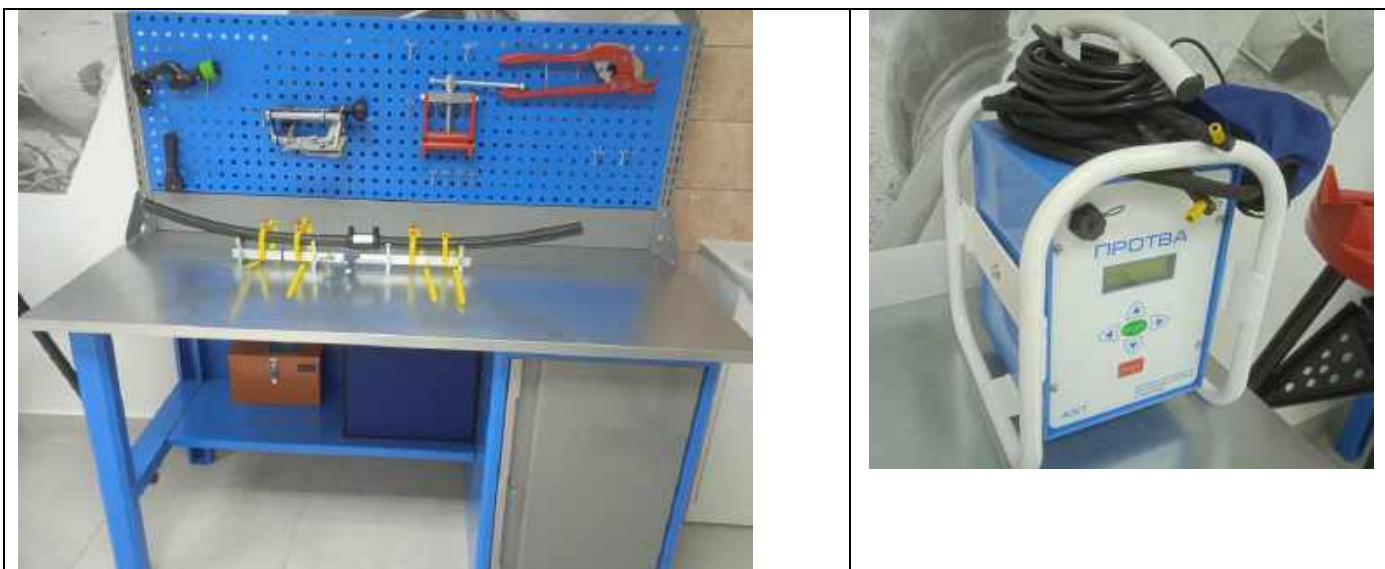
Стенд для изучения методов сварки и подготовки трубопроводов к сварке
